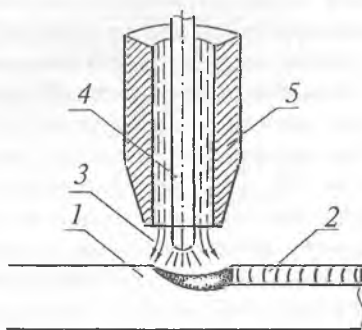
Аргонно-дуговая сварка: 1 — свариваемый узел; 2 — сварной шов; 3 — струя аргона; 4 — плавящийся электрод; 5 — горелка
